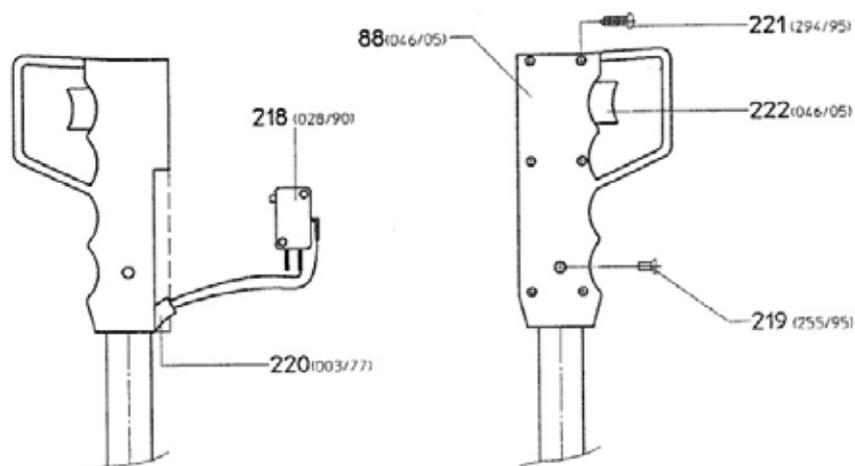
Dessin des pièces détachées 4 - MKS 275 N
